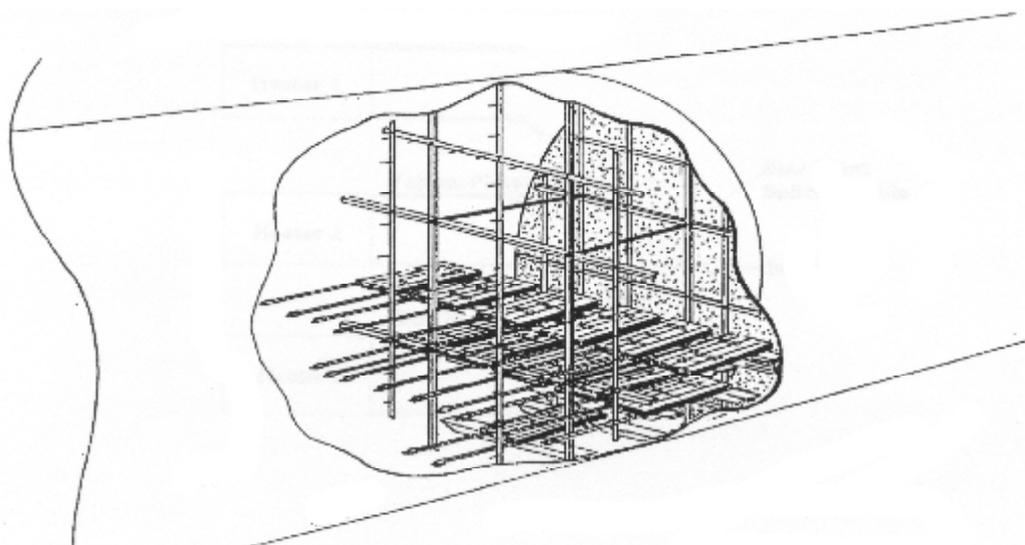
Схема установки желобковых нагревателей при термообработке замыкающего шва корпуса аппарата большого диаметра
